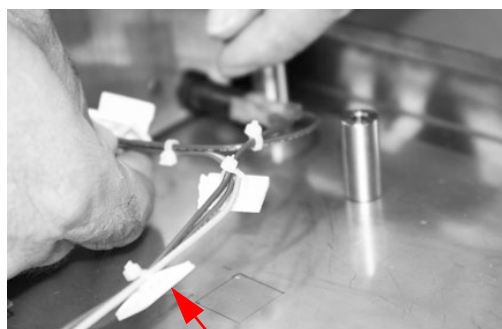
Vuelva a colocar la cubierta de plástico transparente y apriétela suavemente
